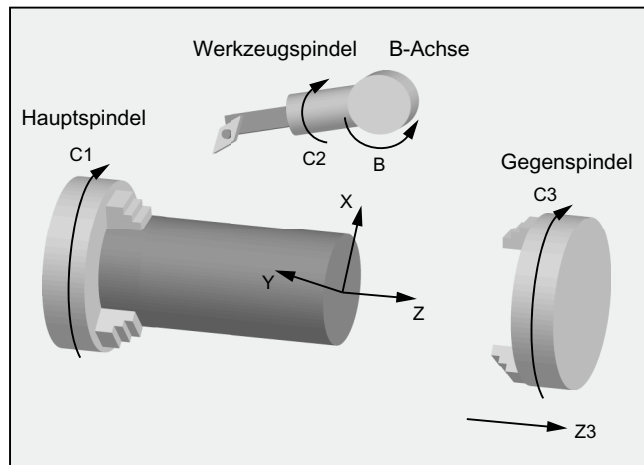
Drehbares Werkzeug bei einer Drehmaschine
